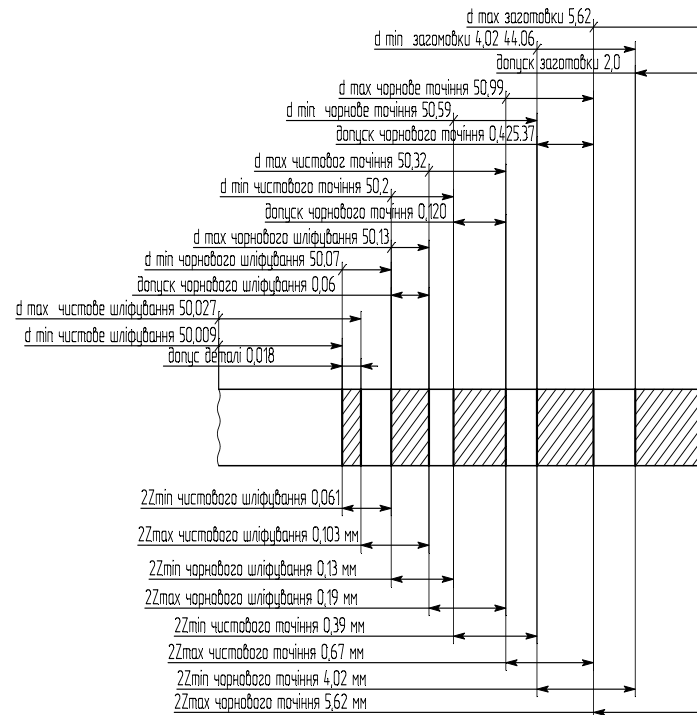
Схема граничного розташування припусків та допусків на обробку поверхні  $\varnothing 50^{+0,027}_{+0,009}$  мм.
